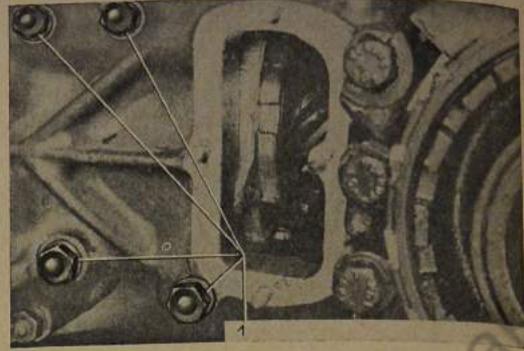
Einstellbuchse für Antriebskegelrad geht schwer
